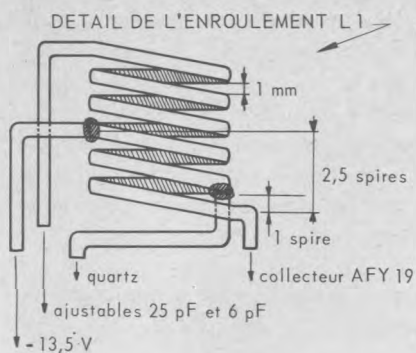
Détail du bobinage haute fréquence de l'émetteur
